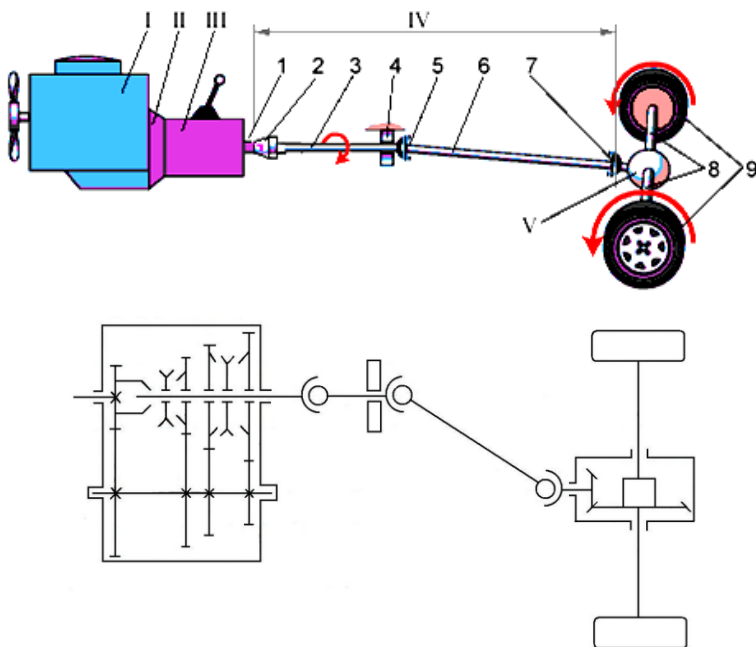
Кінематична схема трансмісії автомобіля ГАЗ-3307: I – Двигун; II – Зчеплення; III – Коробка передач;
